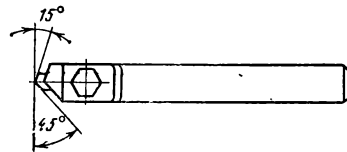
Фреза торцовая с режущими элементами из эльбора-Р:
